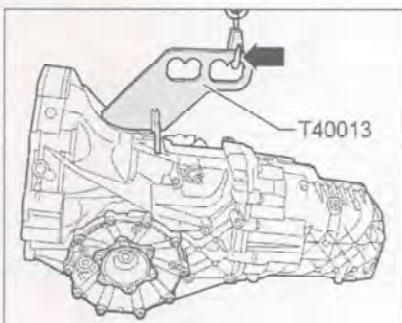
Закрепите приспособление для транспортировки T40013 в отверстии корпуса коробки передач. Подцепите краном устройство для транспортировки за четвертую проушину (стрелка).
